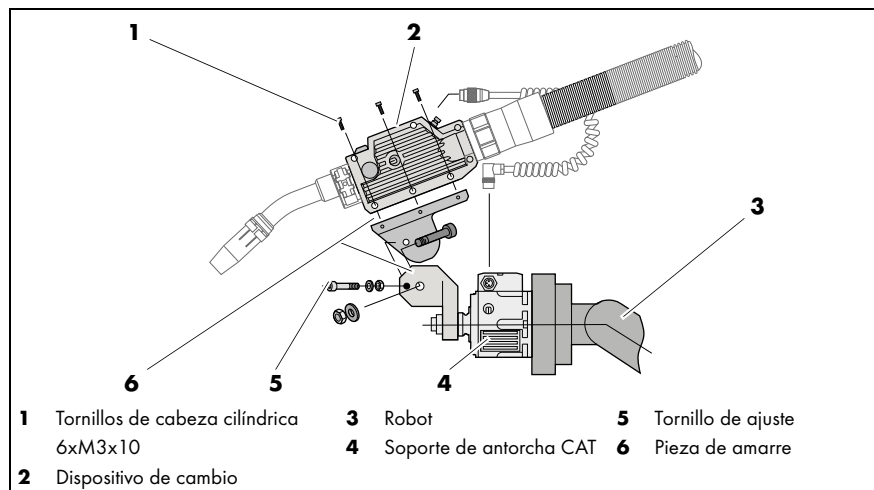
Montar la antorcha de soldadura en el robot
